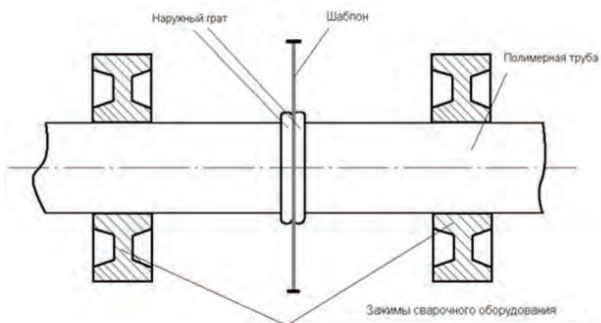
Схема охлаждения сварного соединения с шаблоном под давлением осадки
